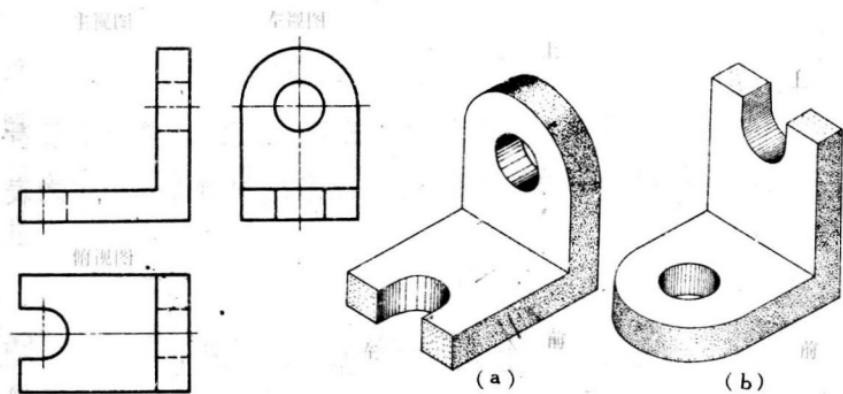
支架的三视图 图 1-16 根据视图特点，摆正支架的位置
